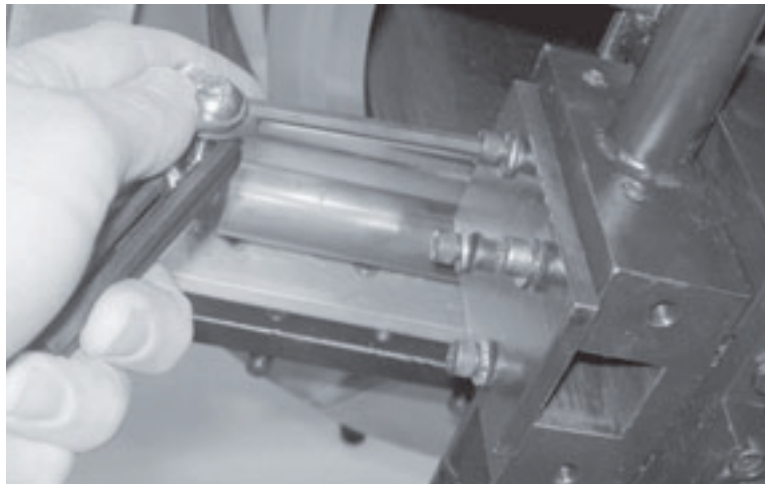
Отверните фиксирующую пластину резцедержателя винты для возможности посадки резцедержателя в суппорте.
